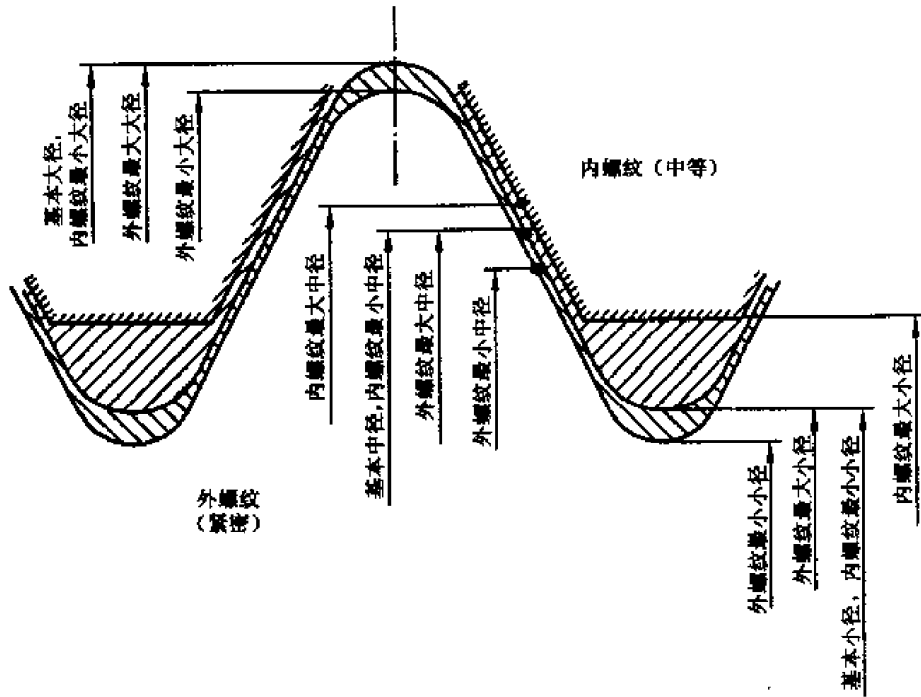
惠氏中等内螺纹与紧密外螺纹配合的公差带位置
